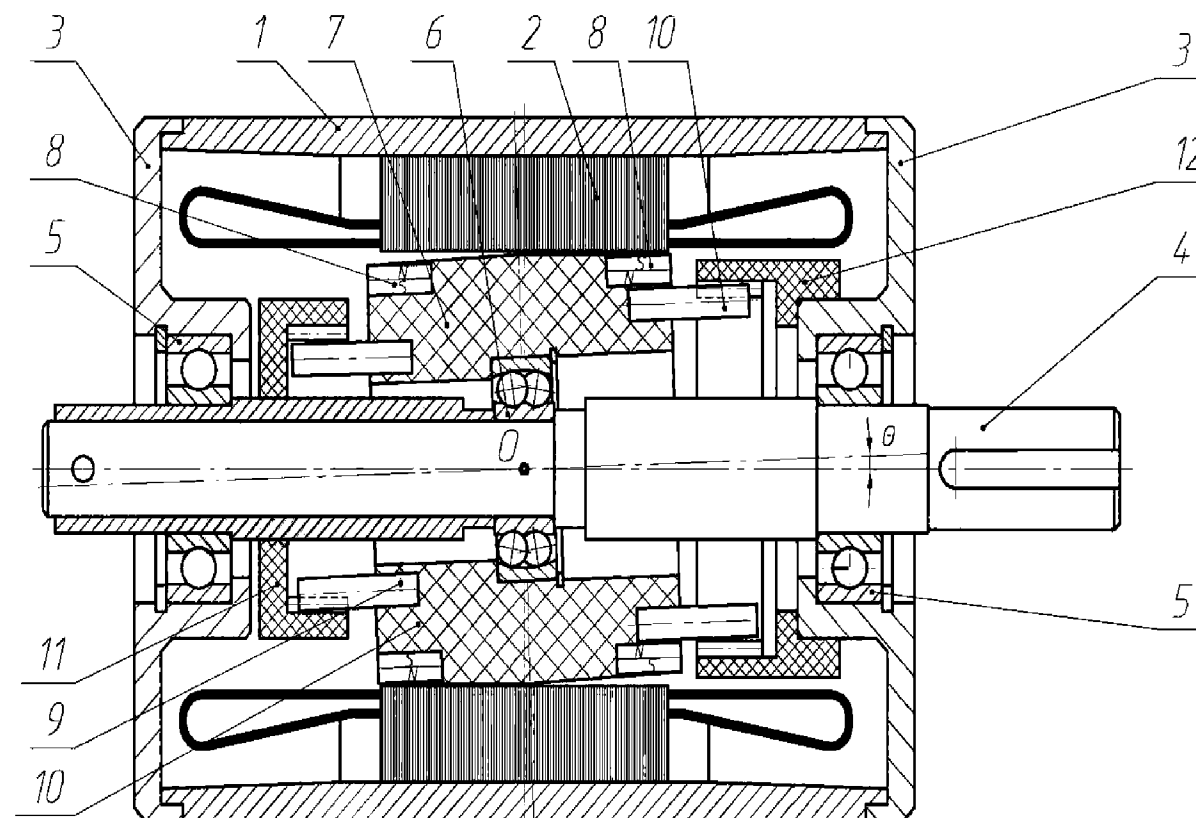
Общий вид конструкции магнитного привода с зубчатым зацеплением прецессионного типа
